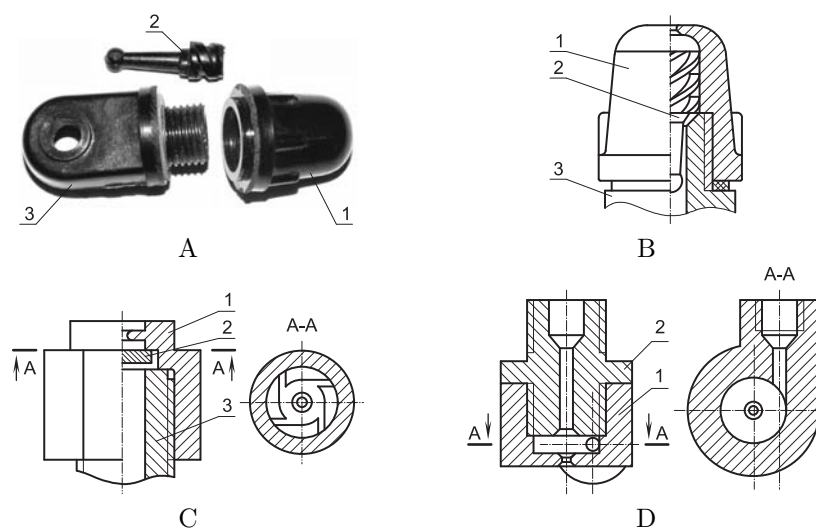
Центробежные распылители: А, В — нерегулируемый с сердечником (А — внешний вид деталей; В — схема строения; 1 — корпус; 2 — сердечник; 3 — подводной патрубков); С — тангенциальный полнопоточный (1 — корпус; 2 — отражатель; 3 — подводной патрубков); D — тангенциальный рециркуляционный (1 — корпус; 2 — штуцер)
